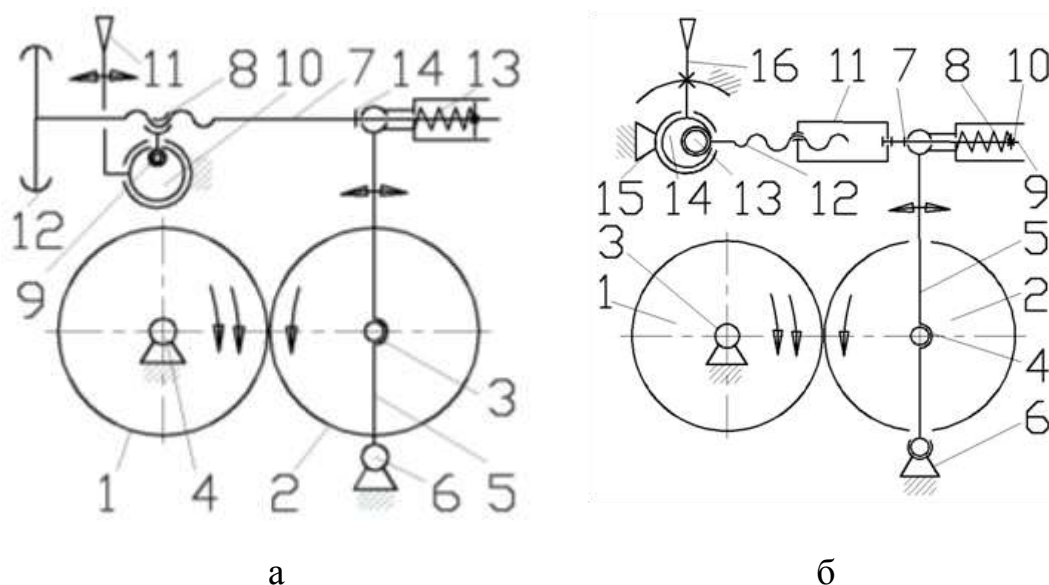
Схеми установчих механізмів вальцьових верстатів.
